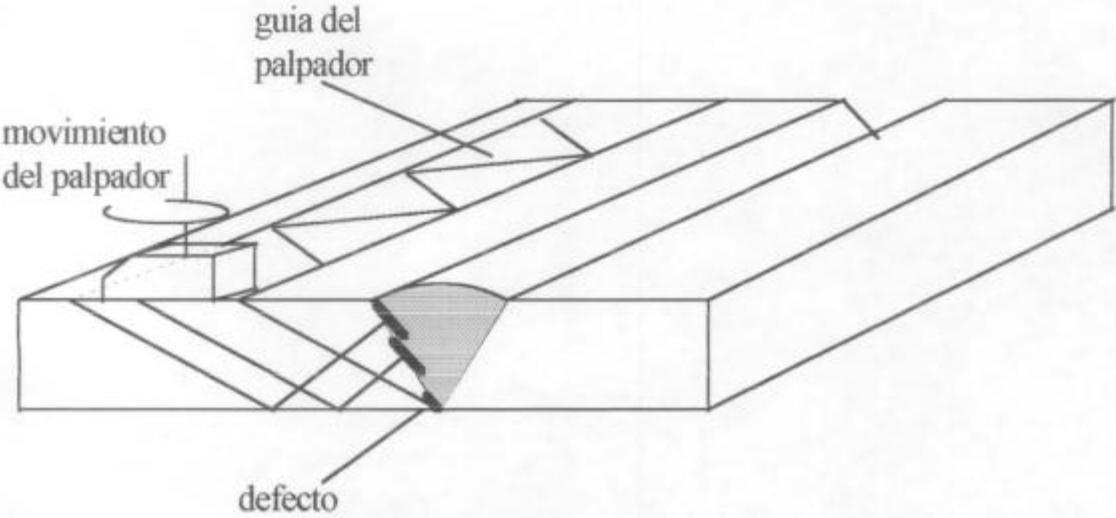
Ensayo de ultrasonido de un cordón de soldadura
